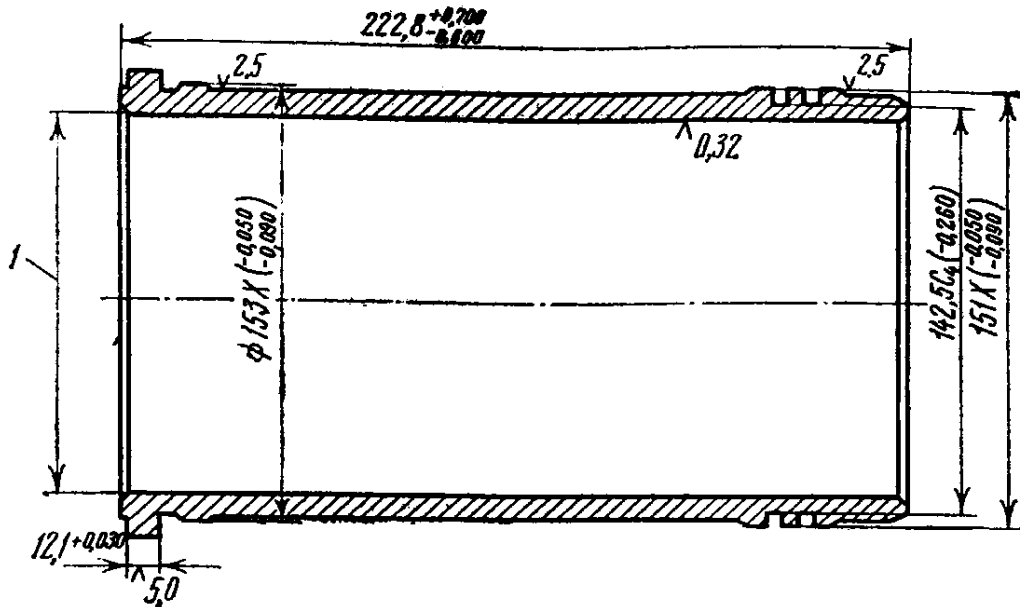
Робоче креслення гільзи циліндрів двигуна СМД
